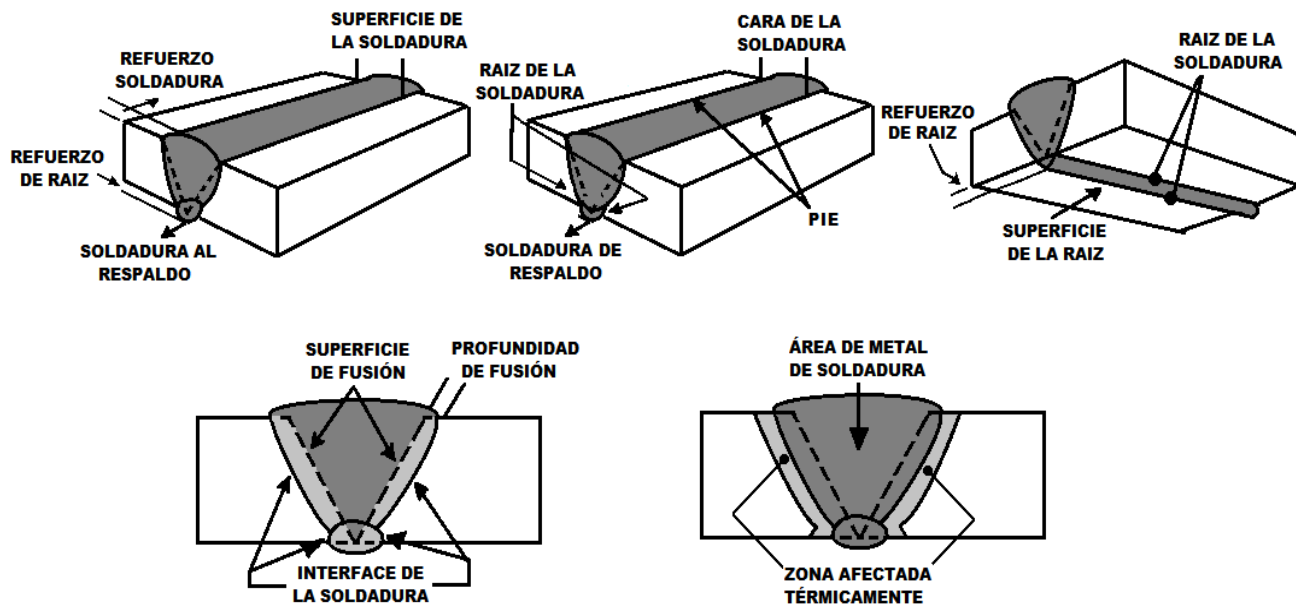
Diferentes partes del cordón de soldadura en bisel (3, 8)
